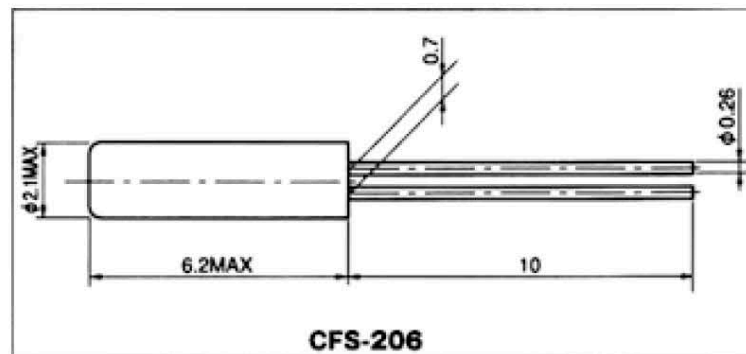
Габаритні розміри кварцового резонатора CFS-206
